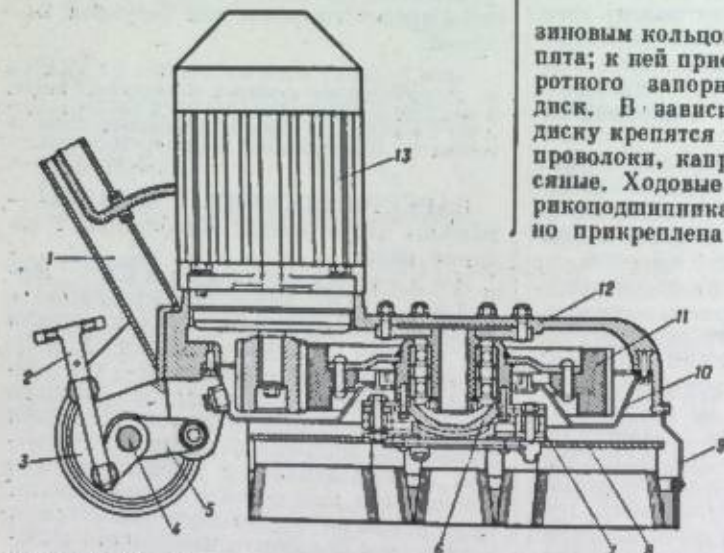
Полотерная машина OM-13: 1 — рукоятка; 2 — винт регулирующего устройства; 3 — ходовое колесо; 4 — ось; 5 — подвеска; 6 — подпятник; 7 — резиновое кольцо; 8 — съемный диск; 9 — защитный кожух; 10 — картер; 11 — большая шестерня редуктора; 12 — корпус; 13 — электродвигатель.
